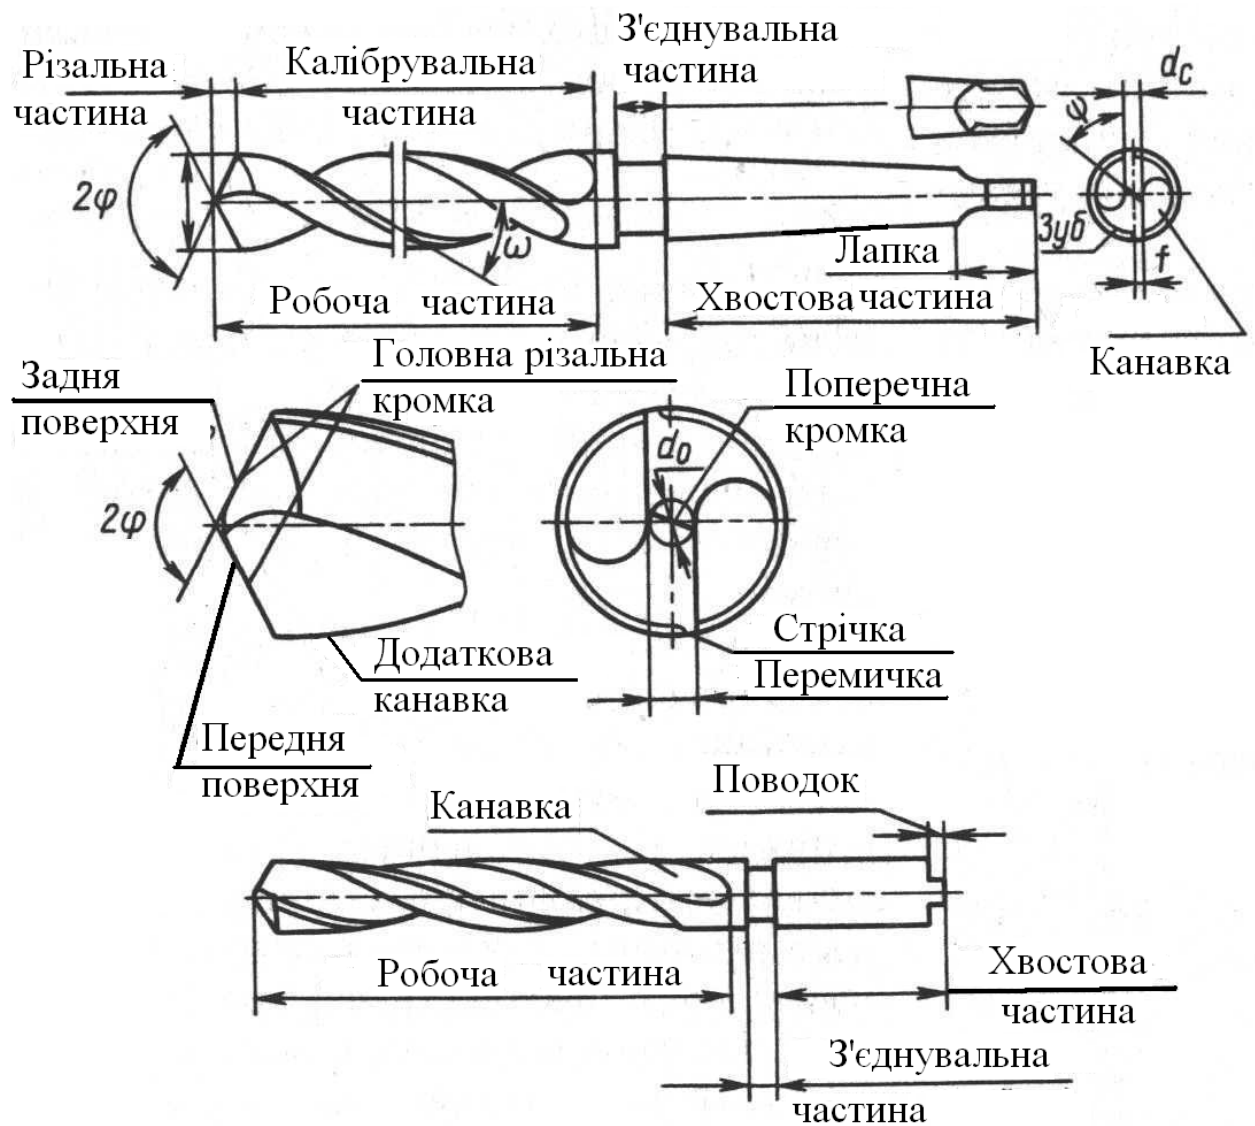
Елементи свердла. L – загальна довжина свердла; l – різальна частина; l_p – робоча частина; l_1 – хвостовик; l_2 – шийка; l_3 – лапка; D – зовнішній діаметр; 1 - головні різальні кромки; 2 - стрічка; 3 - спинка зуба; 4 - гвинтова канавка; 5 - задня поверхня; 6 - передня різальна кромка; 7 - передня поверхня; α - товщина серцевини; f - ширина стрічки; h - висота стрічки.
